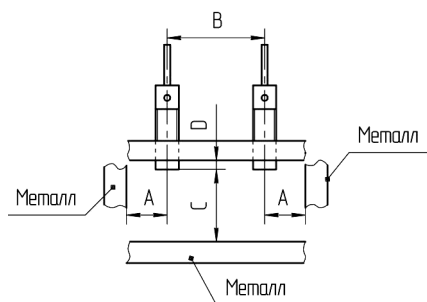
Габаритные и установочные размеры датчиков ДПА-302
